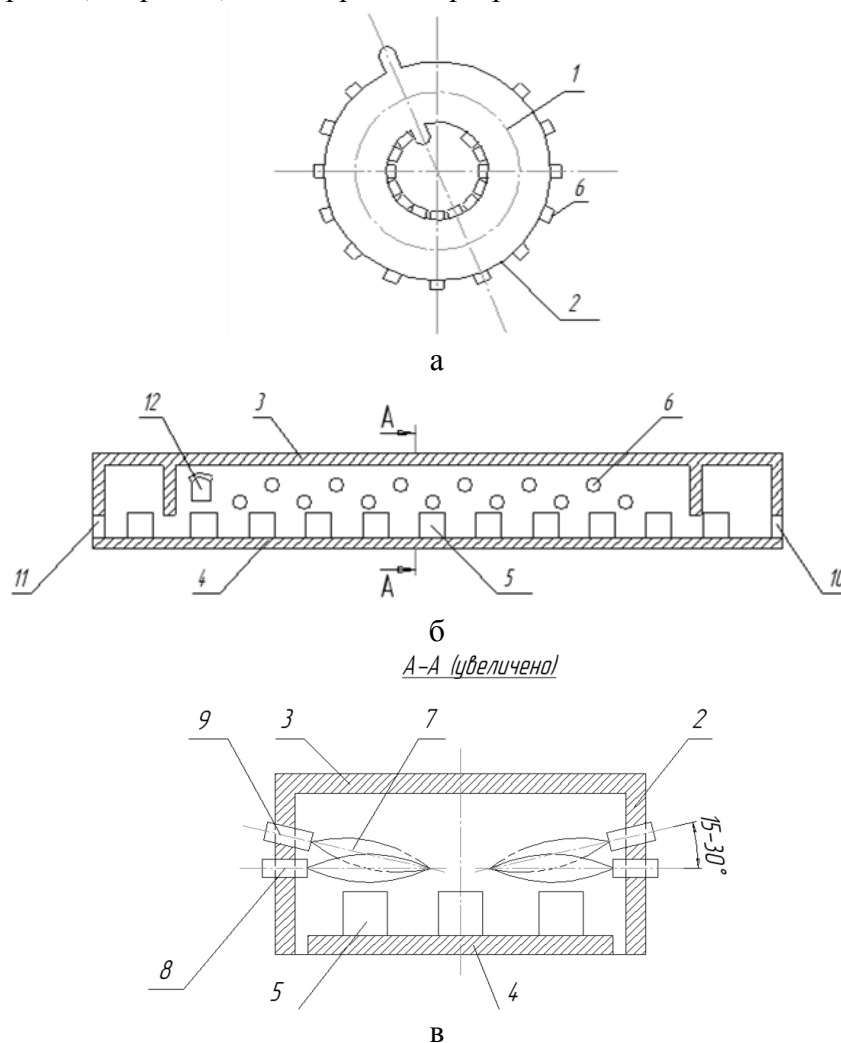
Схема нагревательной печи с кольцевым подом, вид сверху (а), продольный разрез (б), поперечный разрез (в)
